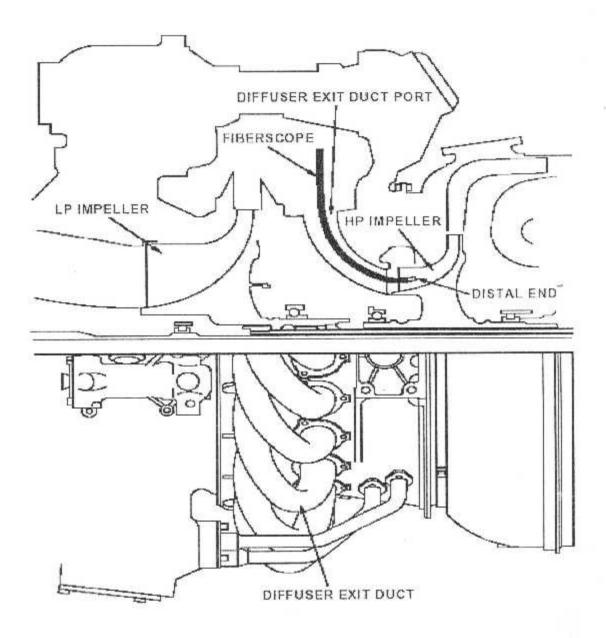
INSPECTION BOROSCOPIQUE DU COMPRESSEUR HP
